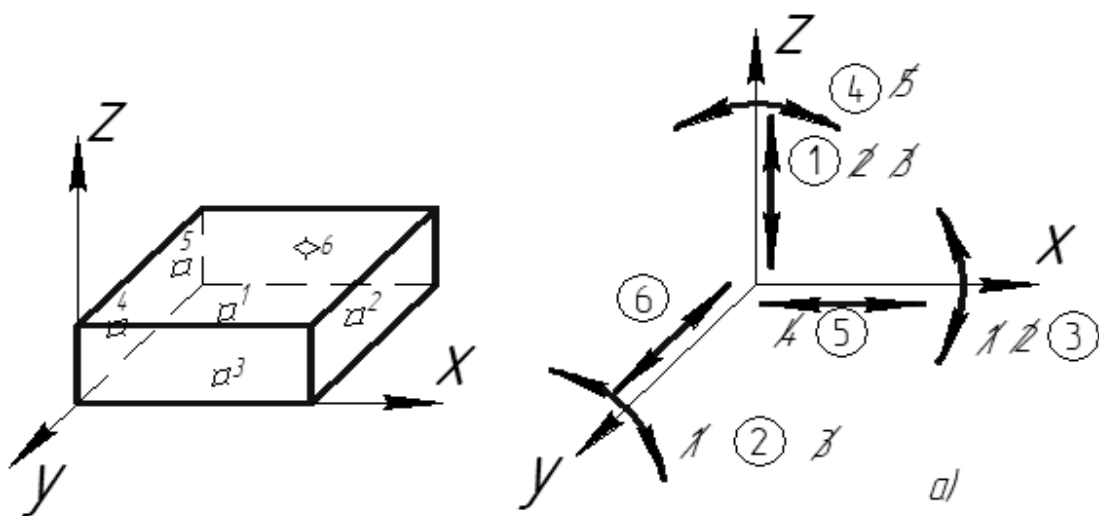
Базування призматичної заготовки в «координатний кут»
